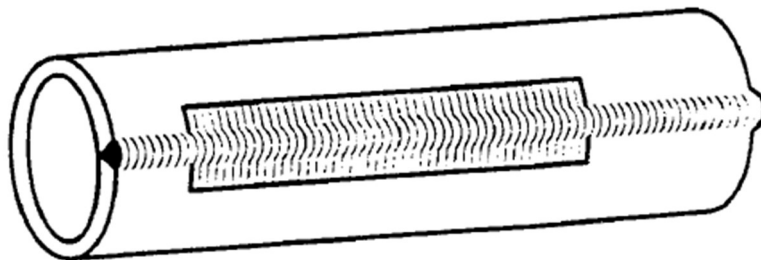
Zkušební vzorek trubky s tupým svarem [37]
